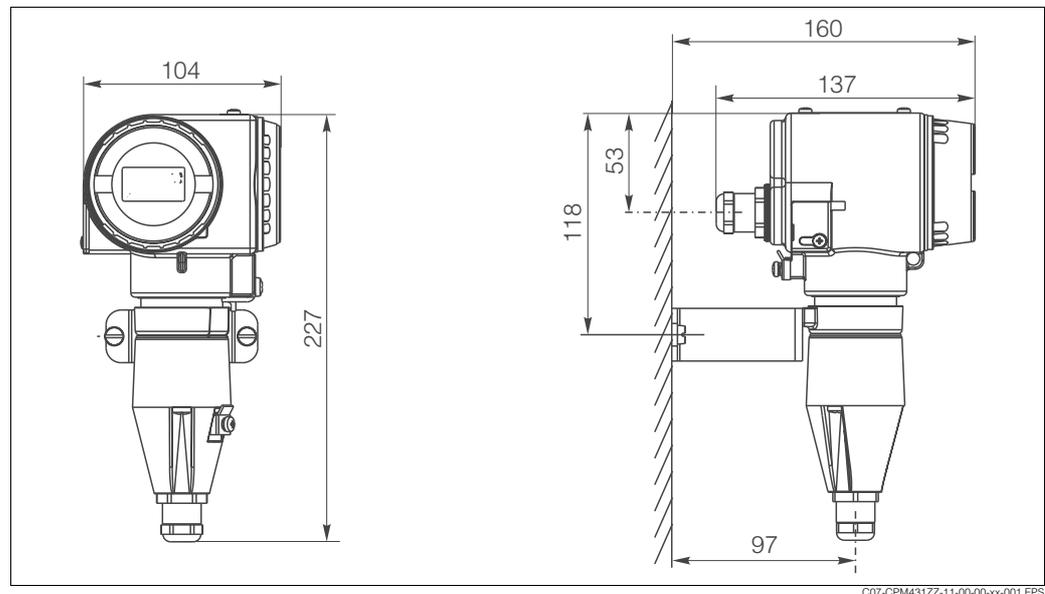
CLM 431 für Wandmontage mit Befestigungsbügel (bei CLM431-xxx2xx im Lieferumfang)
